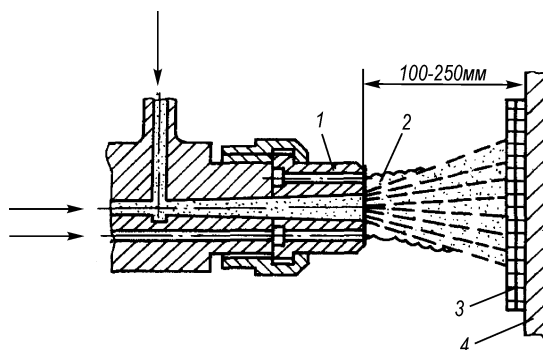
Схема подачи порошка с помощью транспортирующего газа:
